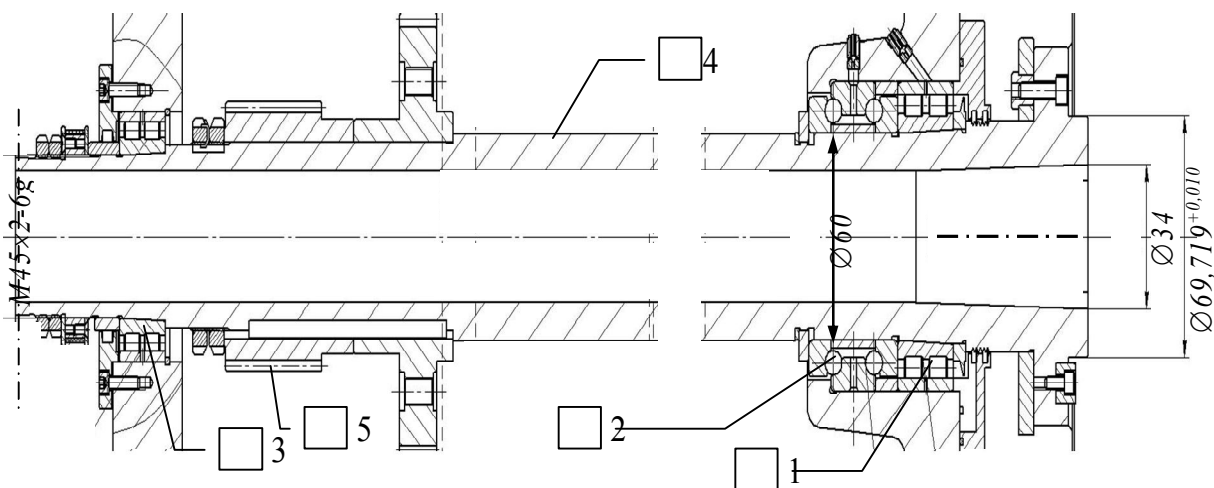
Шпиндель верстата на підшипниках кочення; позиціями показані джерела вібрацій шпинделя
